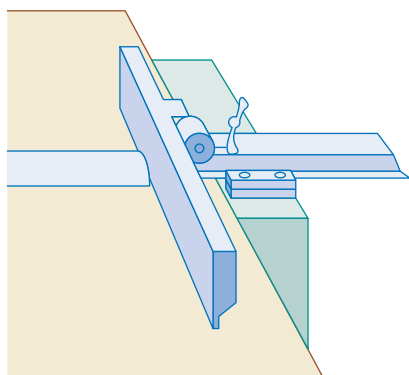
Support du guide et carter de protection monobloc - *Fence support and one-piece protective housing
